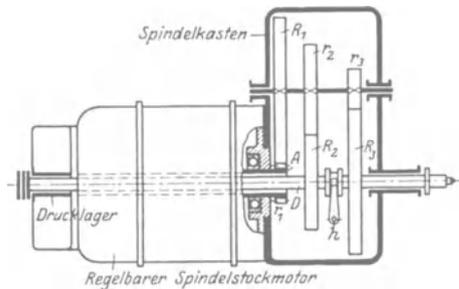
Antrieb mit Einbau- oder Spindelstockmotor.
